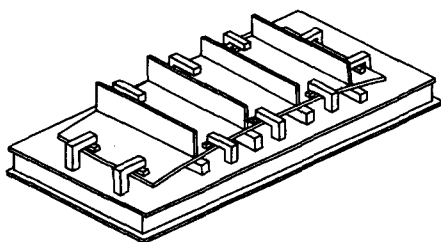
Apparatus for Welding T-Joints Submitted to Elastic Prestrain by Jigs
